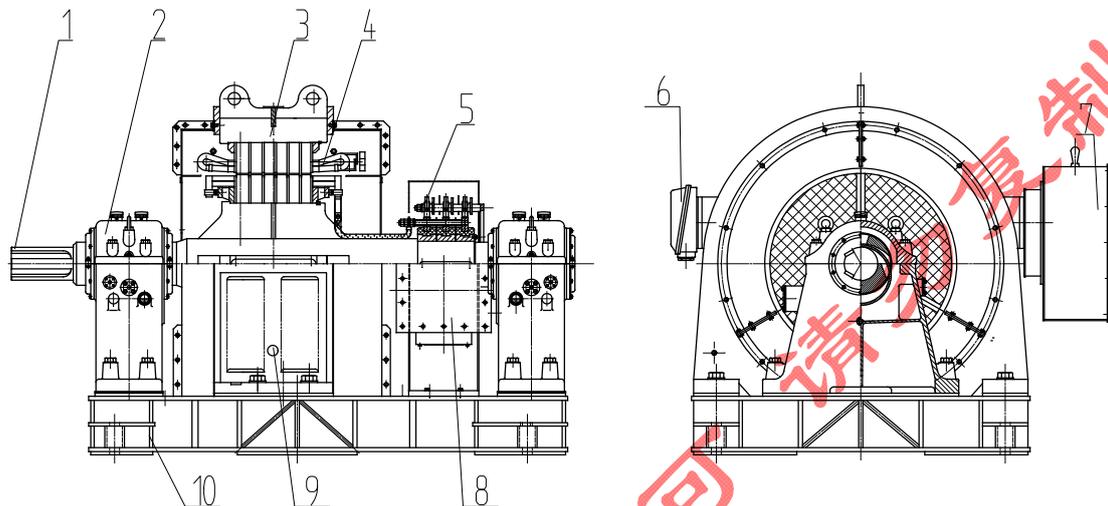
座式滑动轴承电动机结构示意图(主视图半剖)
